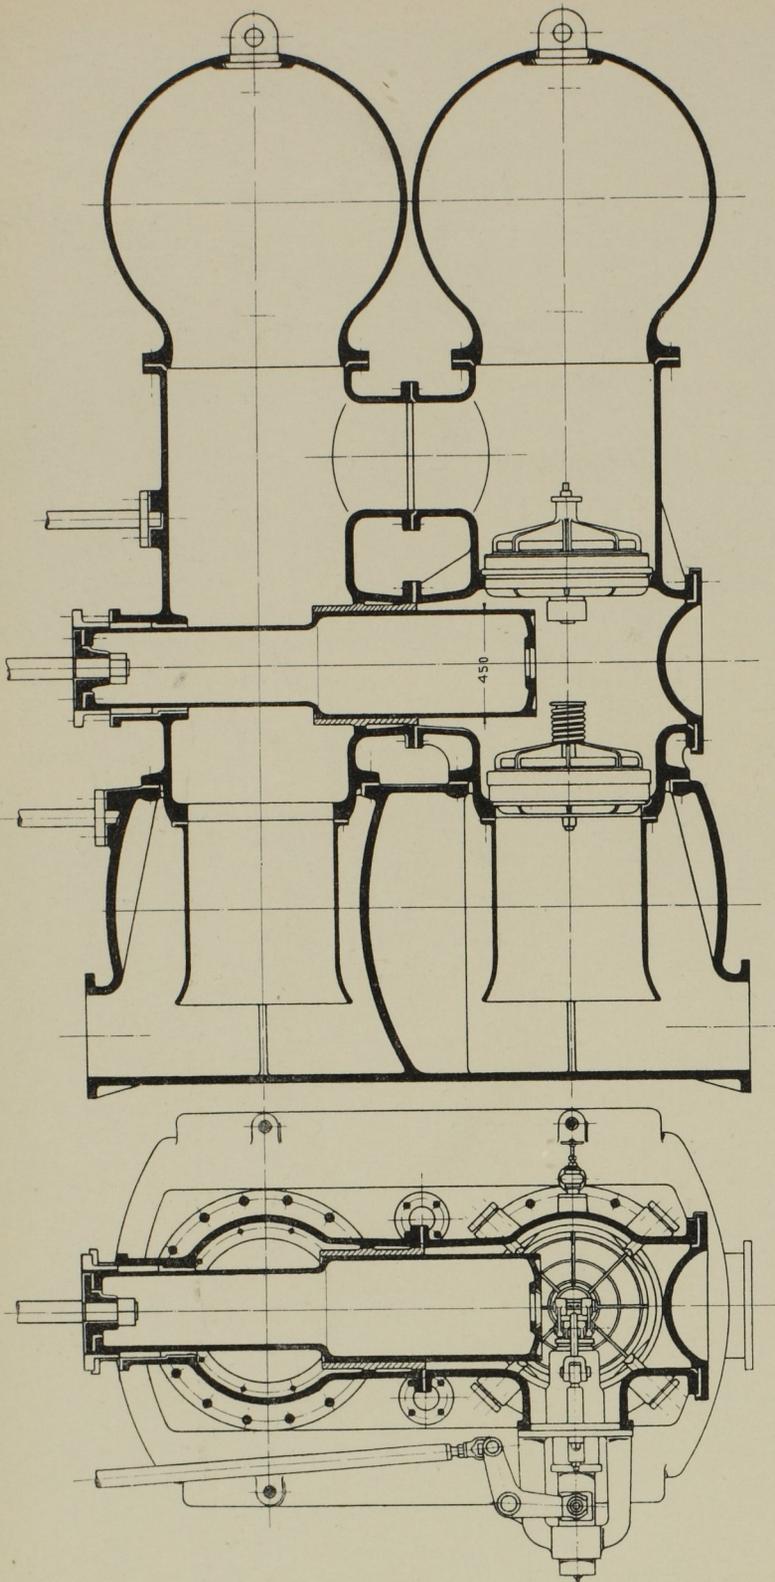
Längsschnitt und Grundriss der Pumpe. Massst. 1:30.
